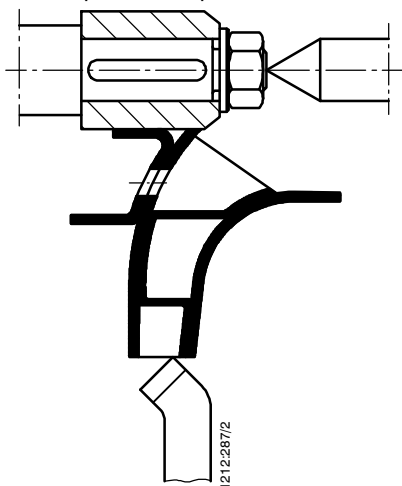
Обтачивание сварного колеса из хромникелевой стали
